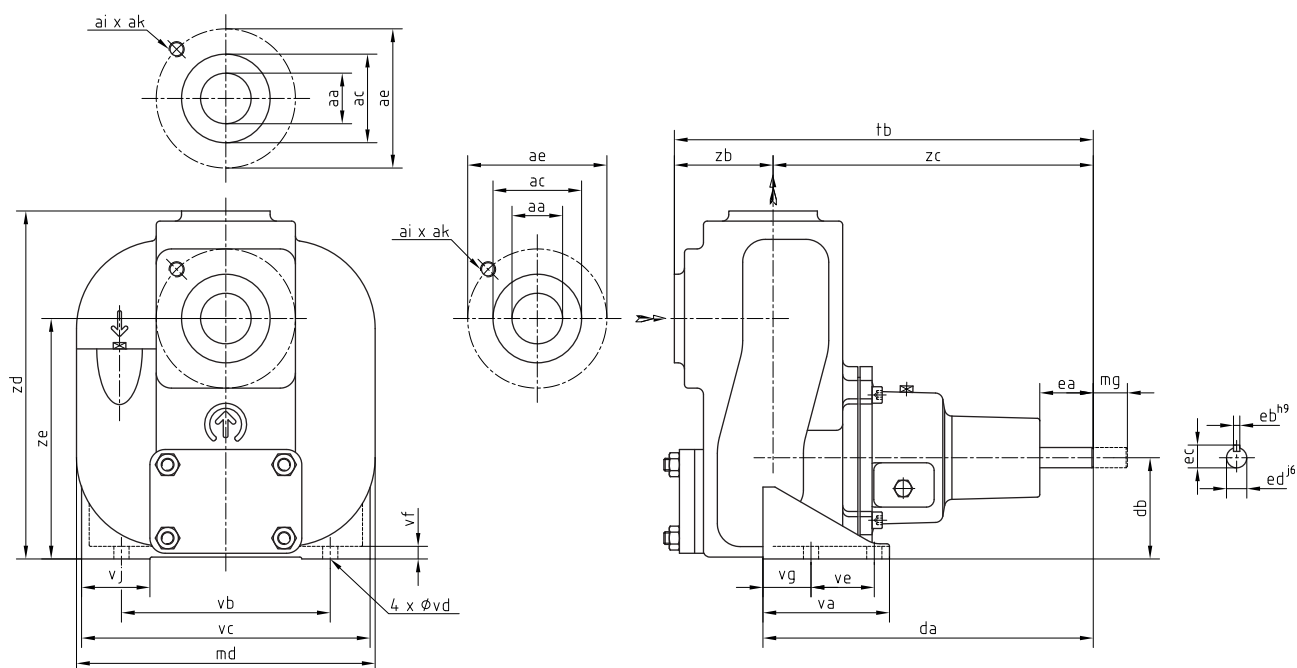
FRE - группы подшипников 1, 2 и 3.
